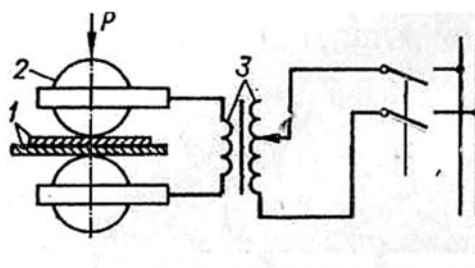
Схема роликовой сварки давлением
